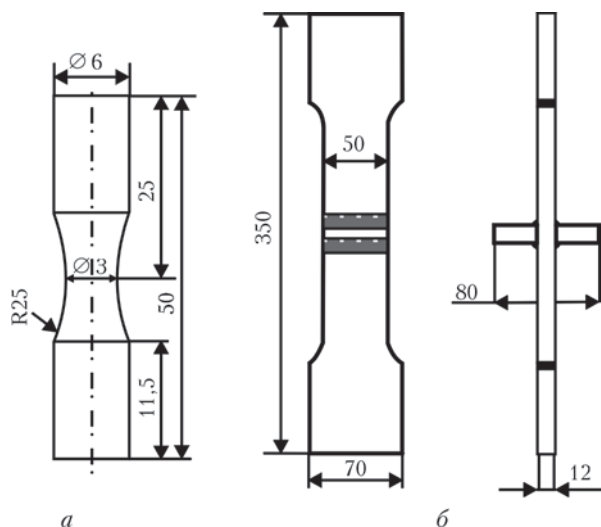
Схематическое изображение образцов для усталостных испытаний; а – круглый галтельный образец; б – образец с тавровыми сварными соединениями для испытаний на усталость в коррозионной среде
